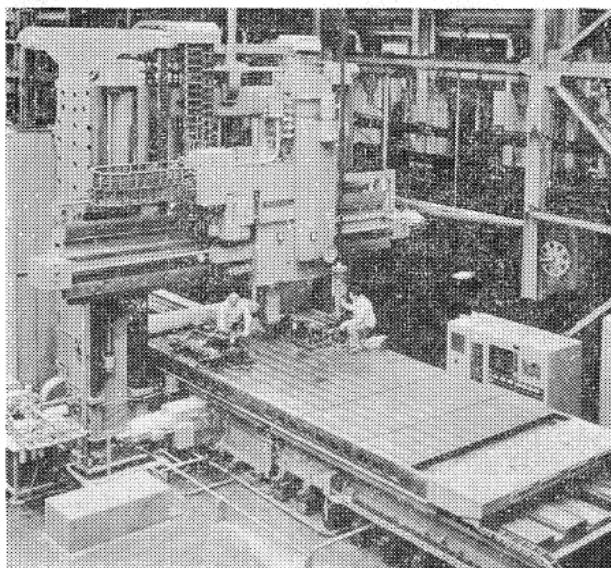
INGERSOLL : ADJUSTABLE RAIL NC MILLING MACHINE 加工容積3,600 mm 幅×3,000mm×7,800mm 長 カッタの上下送りは、クロスレール自身を上下させることによって精密且剛性のある送りがえられるようになっている。NC:GE
